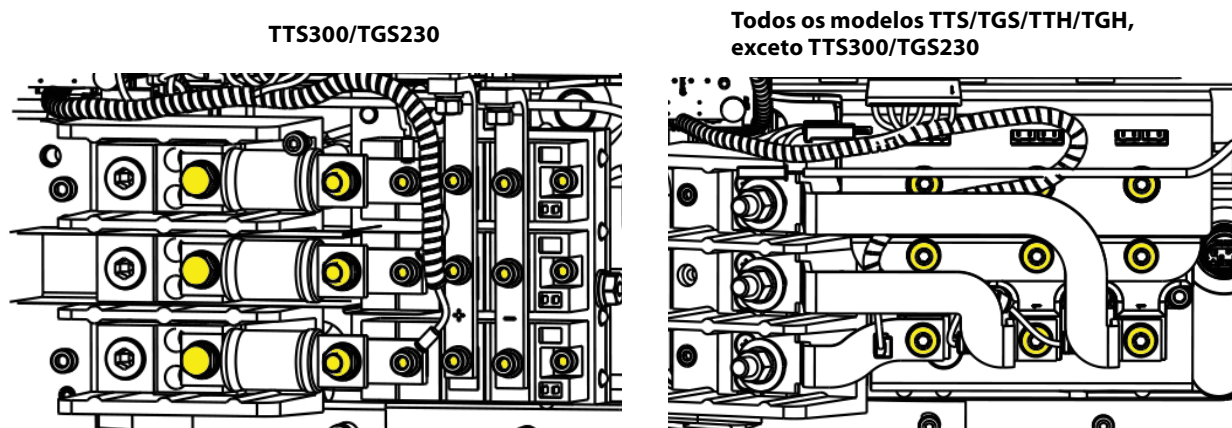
Acesso ao interior do SCR até a presilha do manifolde de refrigeração (apenas compressores TTS e TGS)
